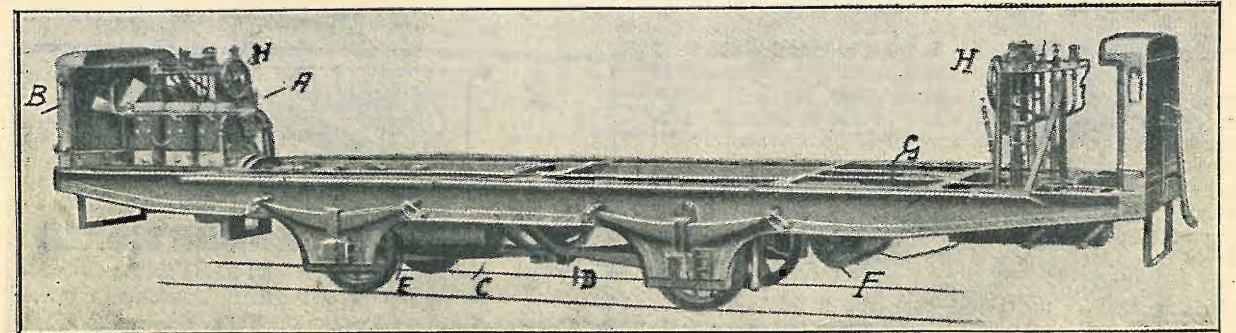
Intelaiatura in ferro col motore, meccanismi e accessori inerenti.
